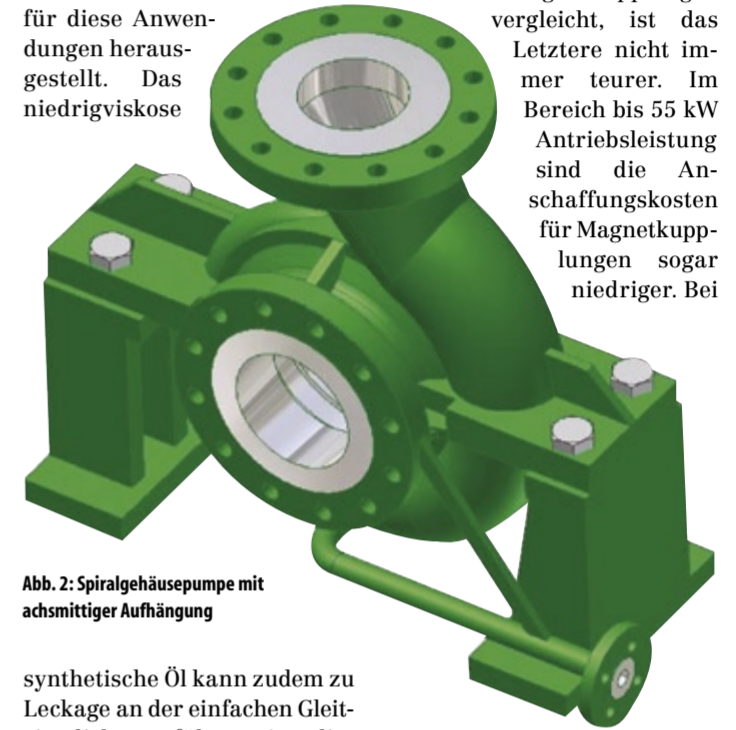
Spiralgehäusepumpe mit achsmittiger Aufhängung
